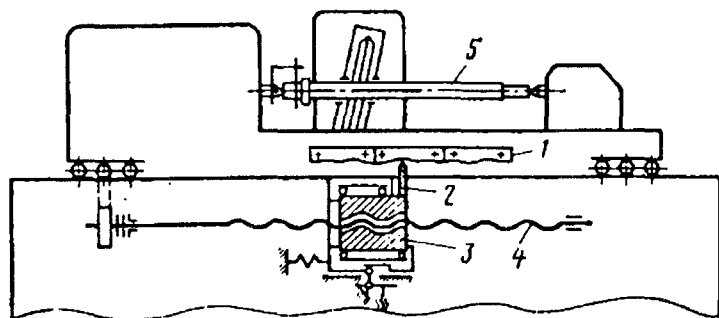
Схема резьбошлифовального станка с системой коррекции
